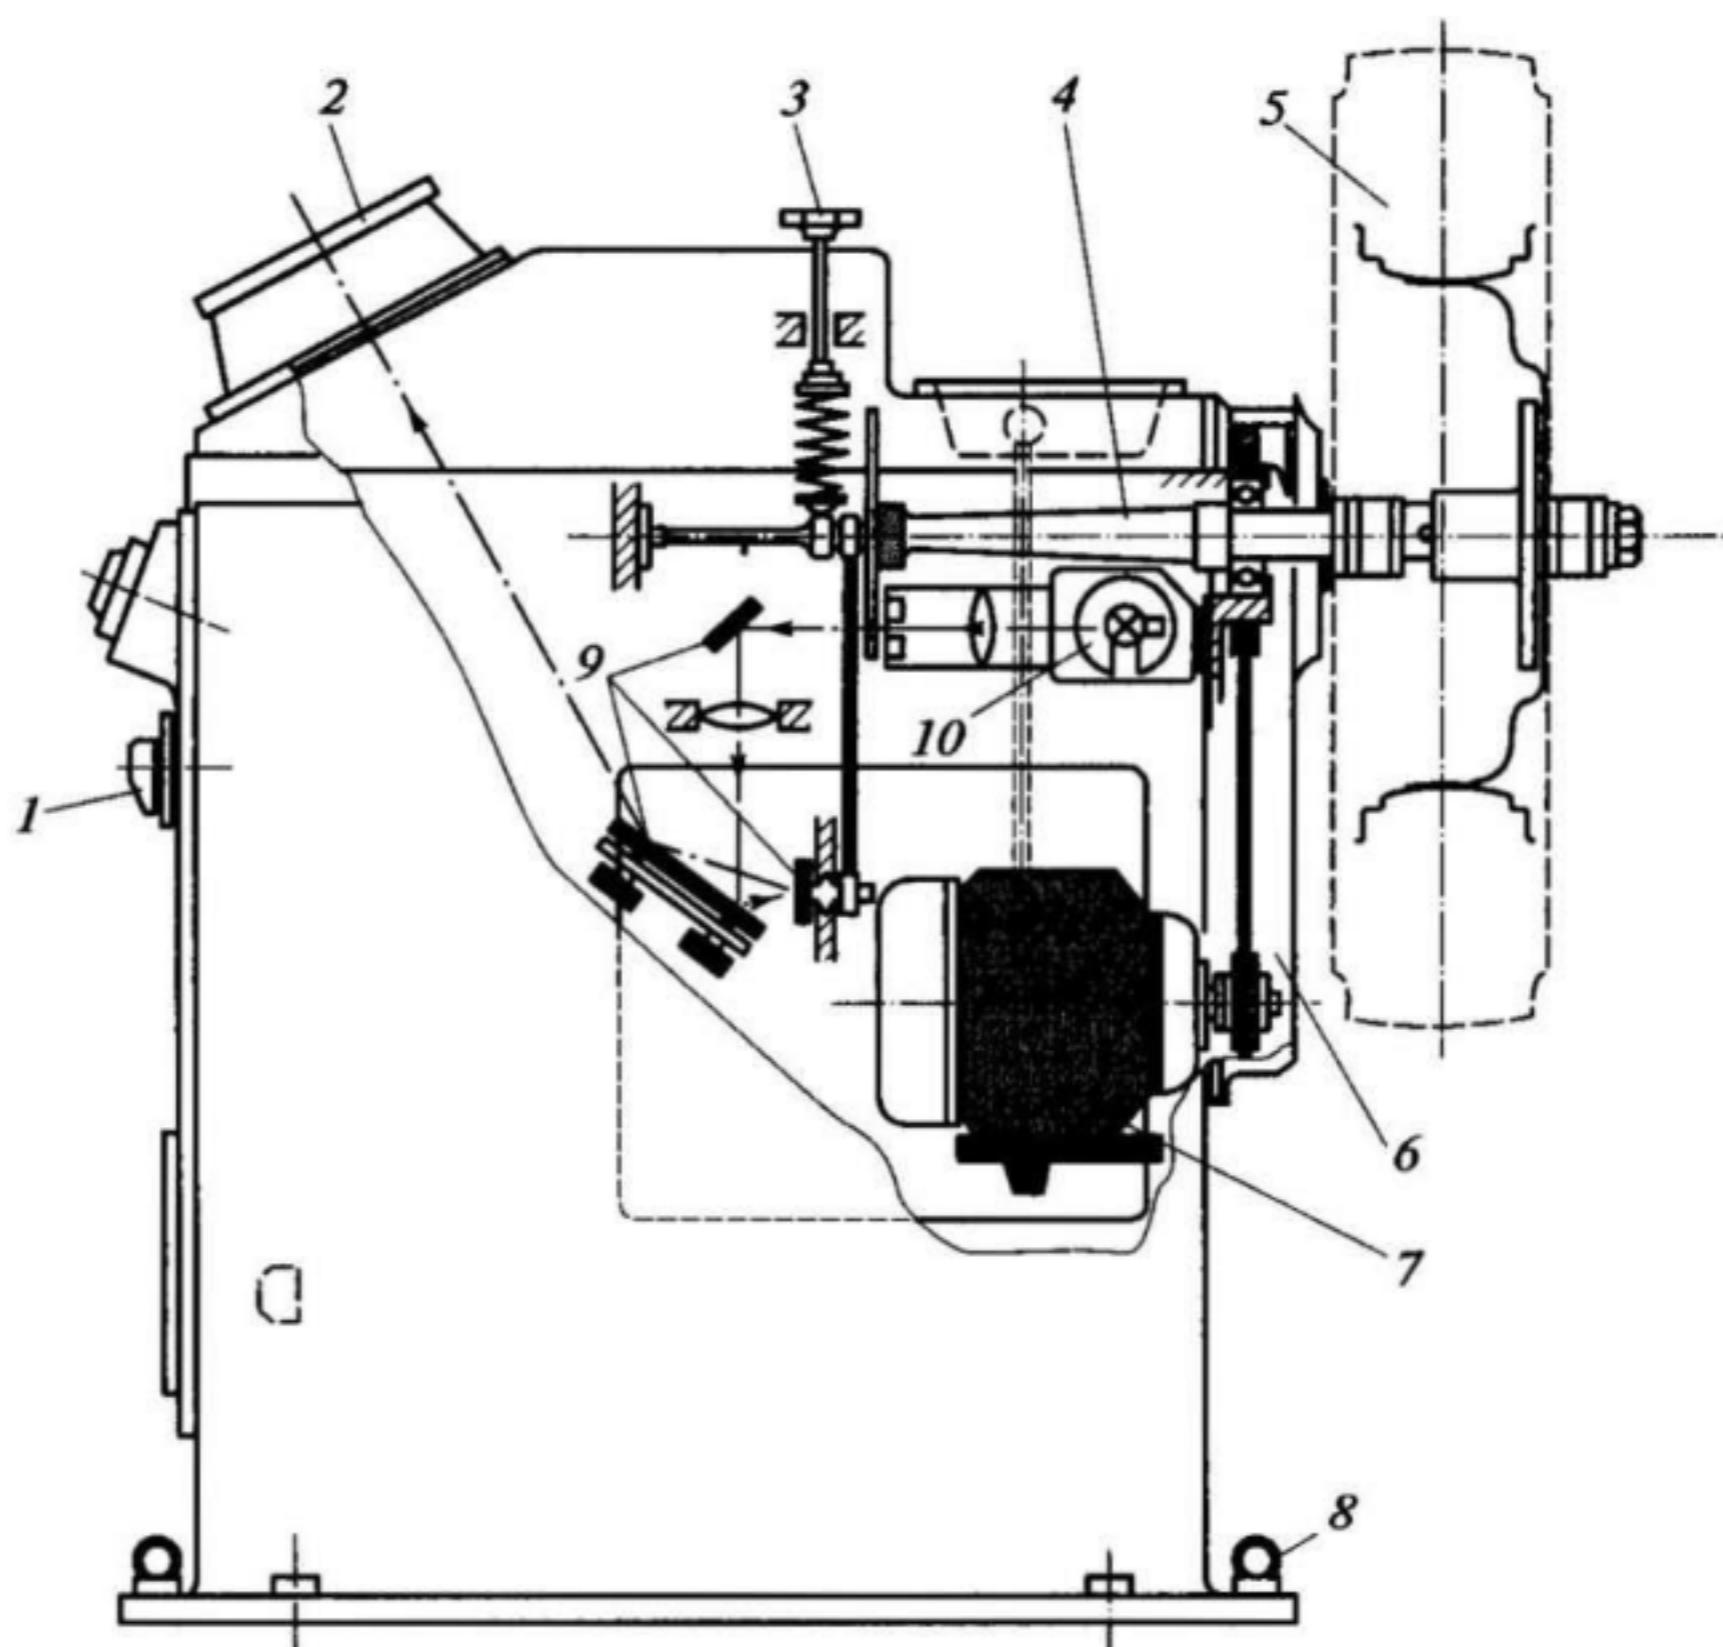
Стенд для балансировки колес, снятых с автомобиля: 1 — выключатель станка; 2 — экран станка; 3 — регулировочный винт; 4 — балансировочный вал; 5 — колесо, снятое с автомобиля; 6 — ремни привода станка; 7 — электромотор привода; 8 — транспортные рым-болты; 9 — зеркала, направляющие отклоненный луч на экран; 10 — источник света
